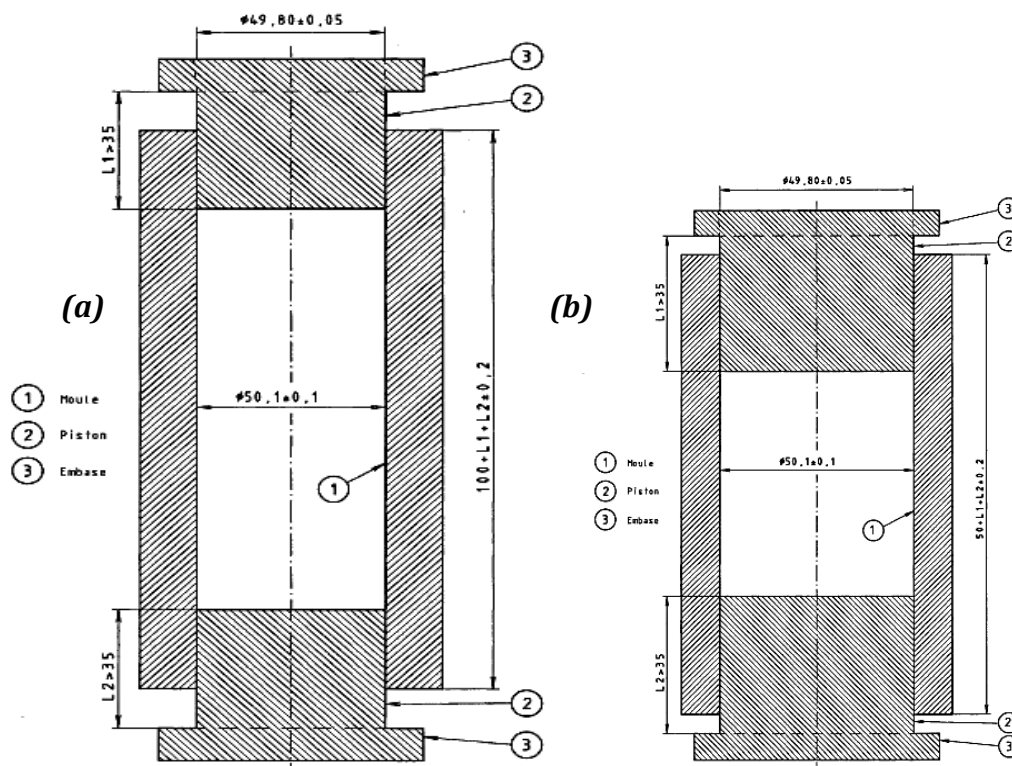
Schéma des moules de compactage utilisés (a) pour éprouvette de 50 mm de diamètre et 100 mm de hauteur et (b) pour éprouvette de 50 mm de diamètre et 50 mm de hauteur.
